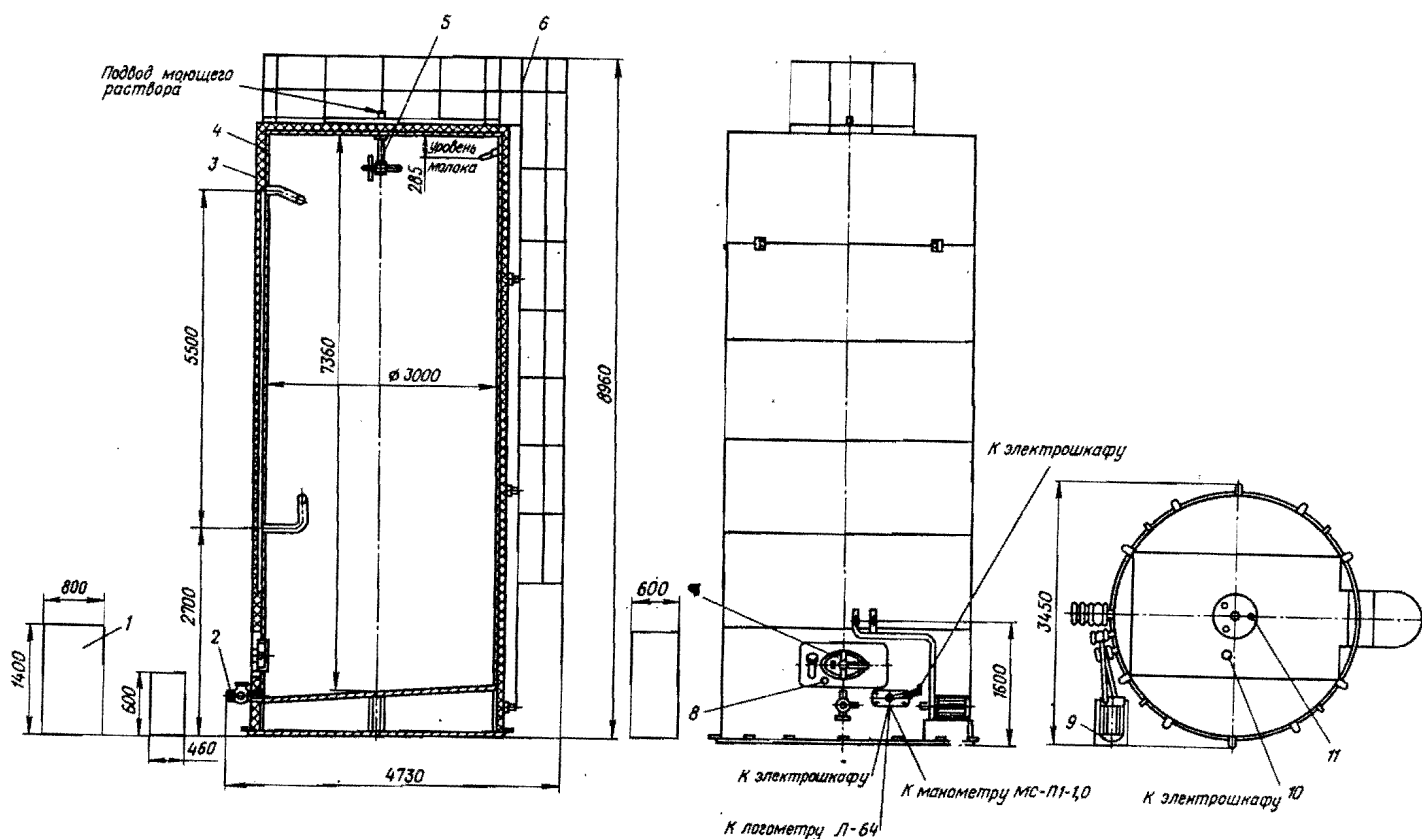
Общий вид резервуара марки В2-ОХР-50:
